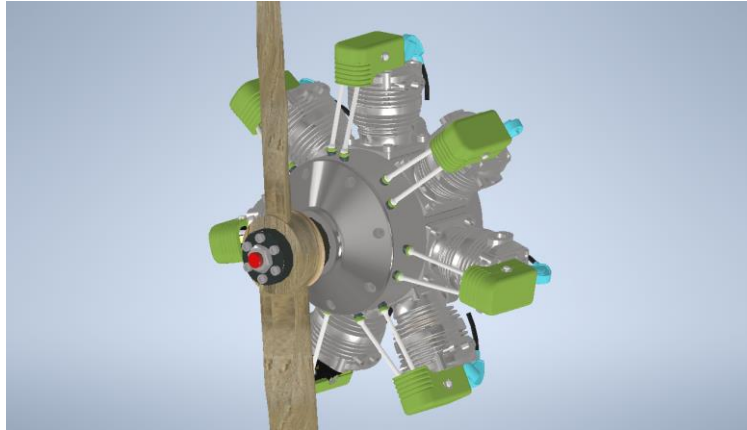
"Ensam parte delantera motor" desde vista frontal
